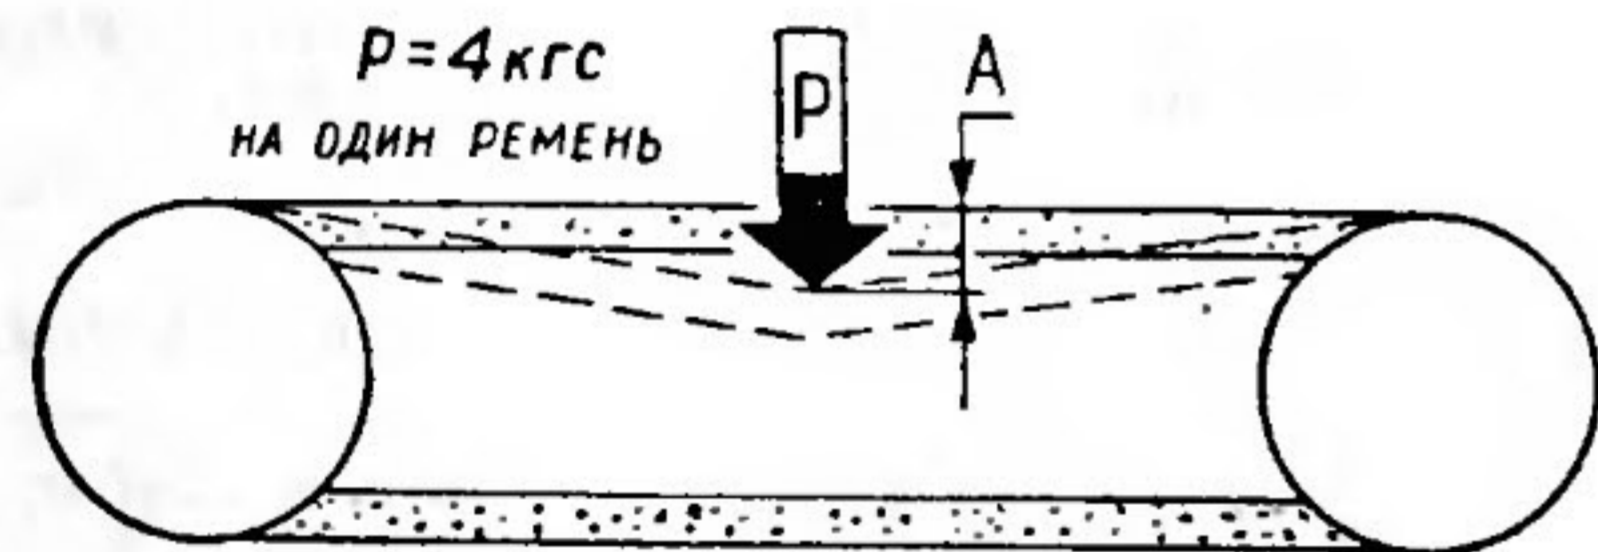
Схема натяжения ремней привода редуктора и вентилятора
